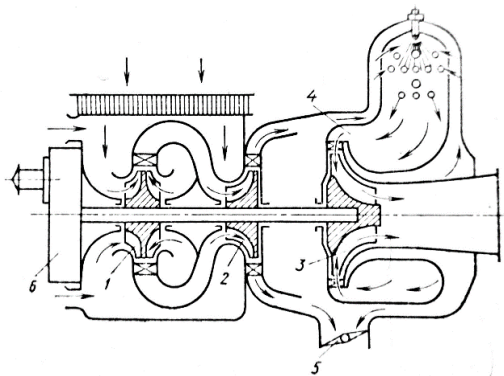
Конструктивная схема ВСУ: 1 и 2 — I и II ступени компрессора; 3 — турбина; 4 — камера сгорания; 5 — Заслонка, регулирующая отбор воздуха; 6 — редуктор
